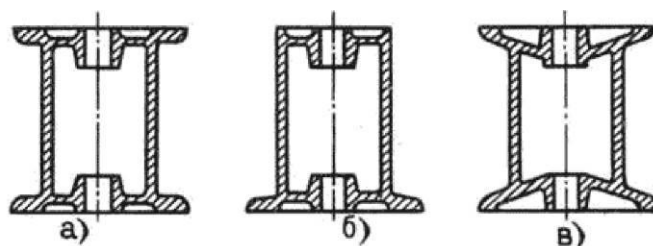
Конструкции литых деталей, снижающие усадочные напряжения в отливках
